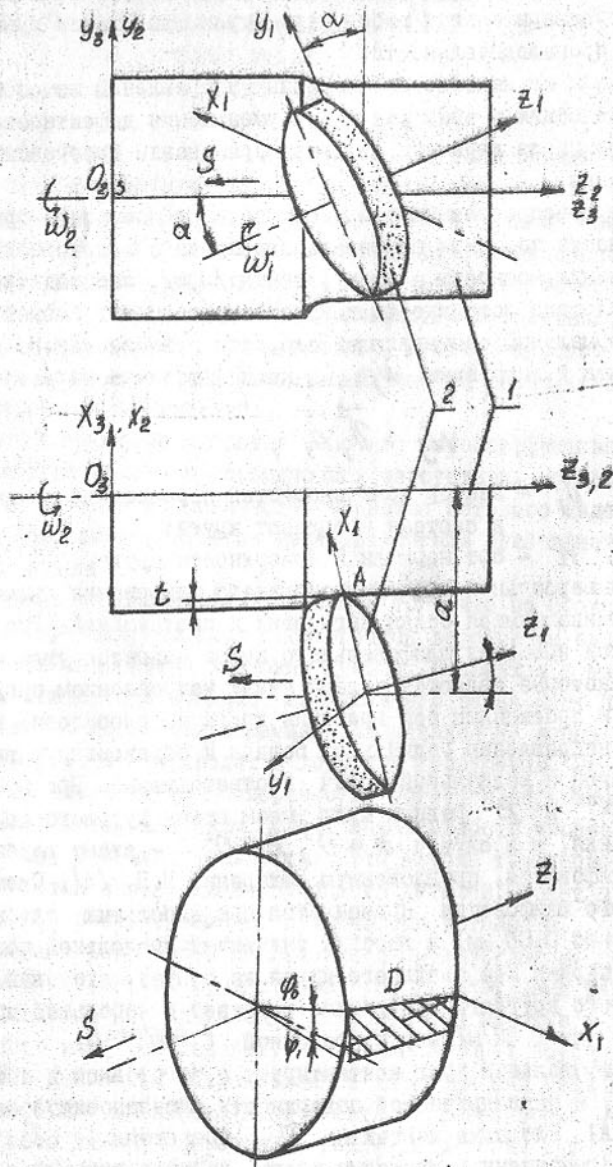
Схема шлифования со скрещивающимися осями заготовки и инструмента
